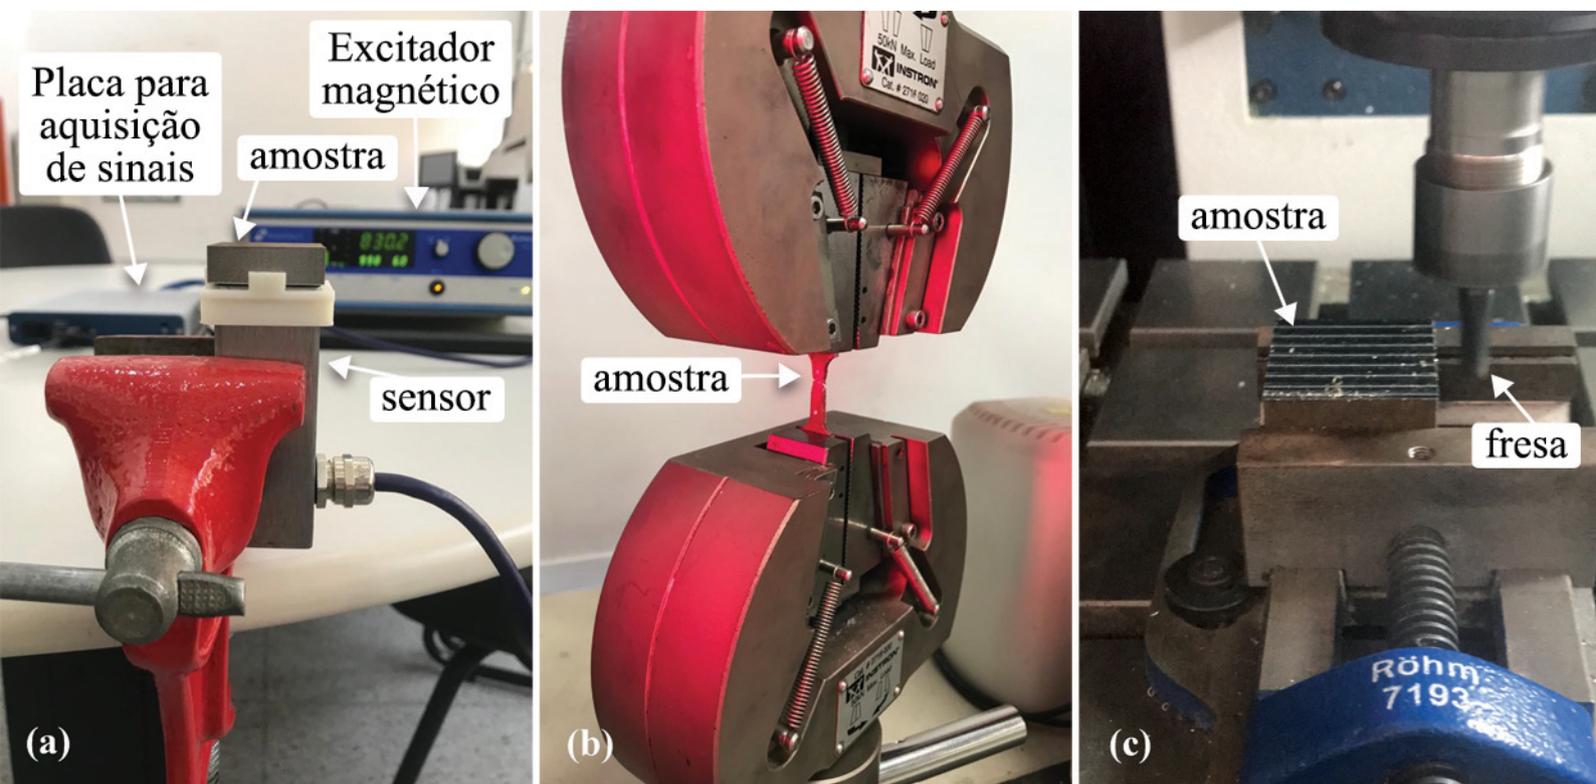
Montagem experimental para: (a) medição do ruído magnético de Barkhausen; (b) ensaio de tração; (c) fresamento das peças de aço maraging produzidas por manufatura aditiva - Fonte: autores.
